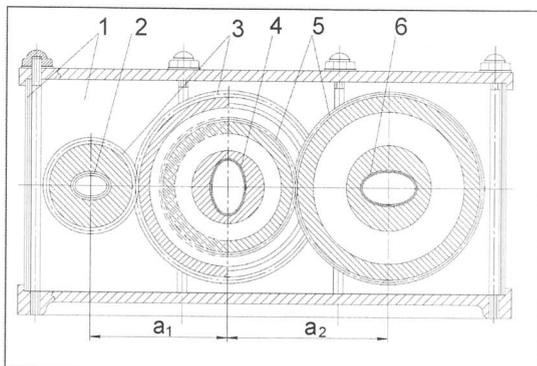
Адаптивный редуктор, поперечный разрез: 1 — навитой корпус; 2, 4, 6 — навитые валы; 3, 5 — зубчатые передачи.
